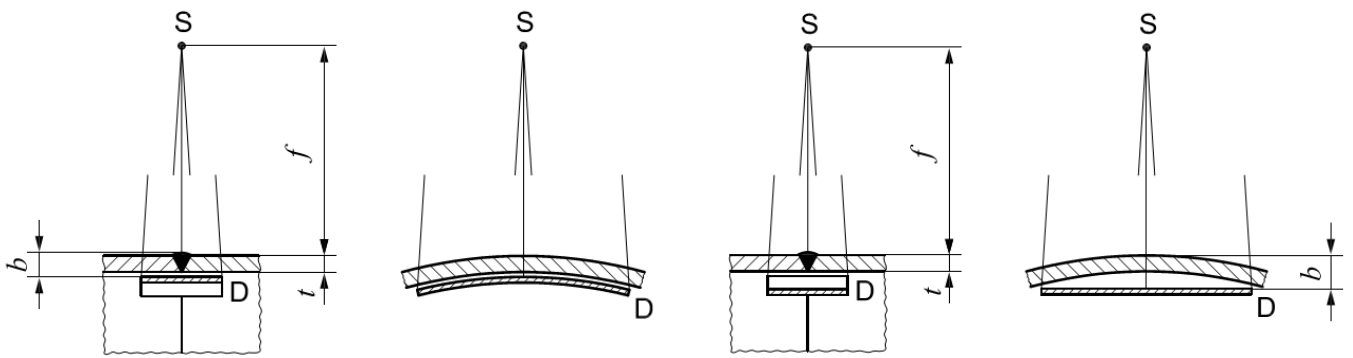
Схема контроля для плоского сварного шва при просвечивании через одну стенку
